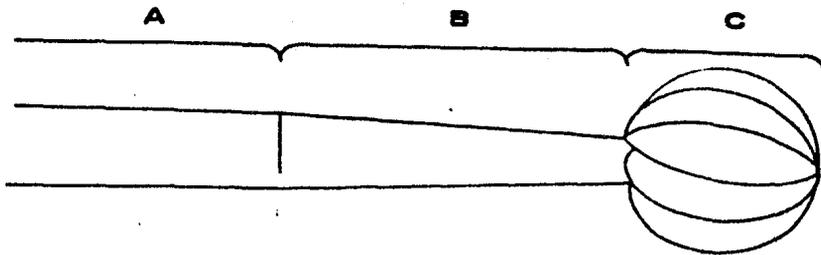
DISTINTAS PARTES DE UNA FRESA
